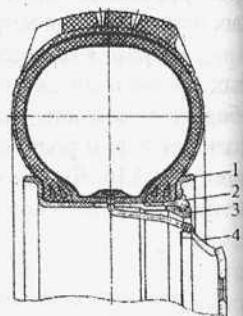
Колесо грузового автомобиля в сборе с пневматической шиной: 1 – кольцо бортовое неразрезное съемное; 2 – пружинное разрезное кольцо; 3 – обод; 4 – диск; 5 – пневматическая шина
